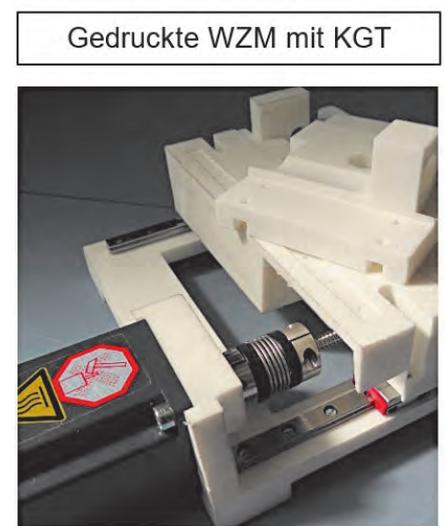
Gedruckte Werkzeugmaschine mit Kugelgewindeantrieb
